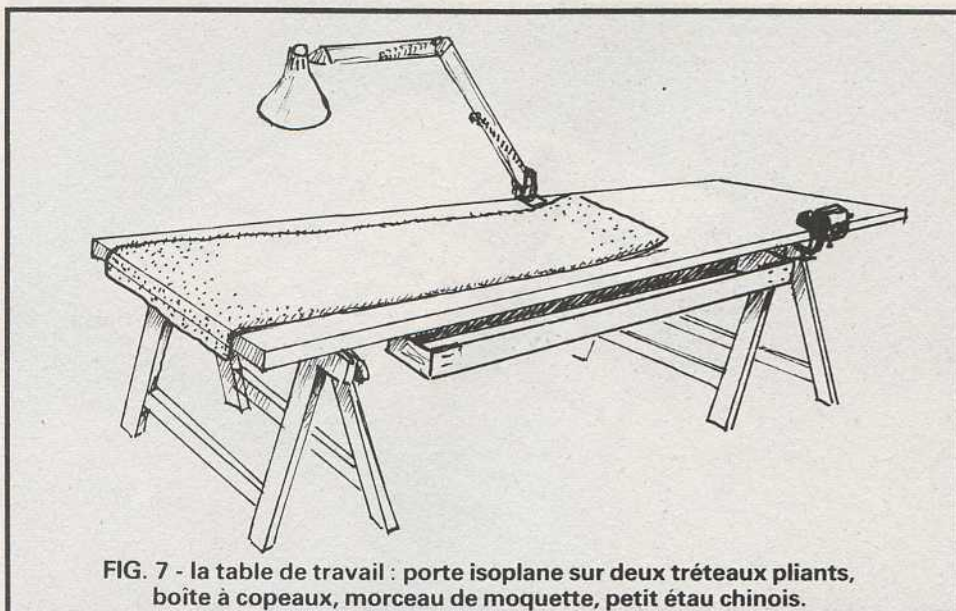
la table de travail : porte isoplane sur deux tréteaux pliants, boîte à copeaux, morceau de moquette, petit étau chinois.
